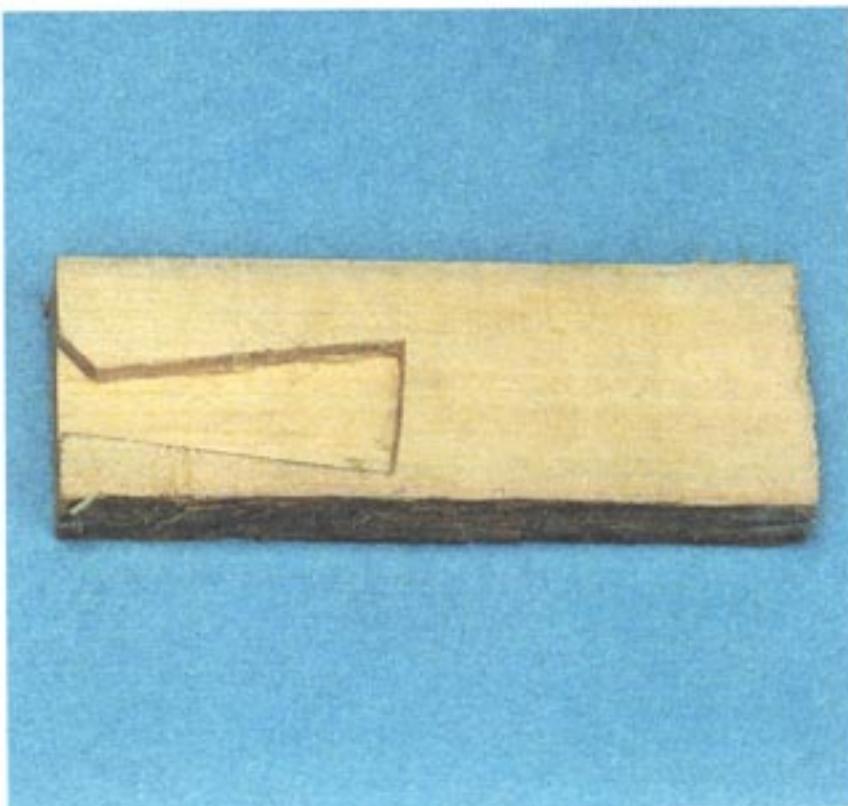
Вырезанный паз под лезвие ножа-косяка в заготовке ручки
